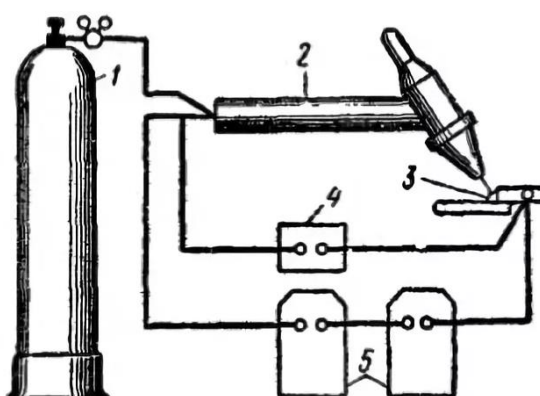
Упрощенная схема ручной аргонодуговой сварки переменным током:
